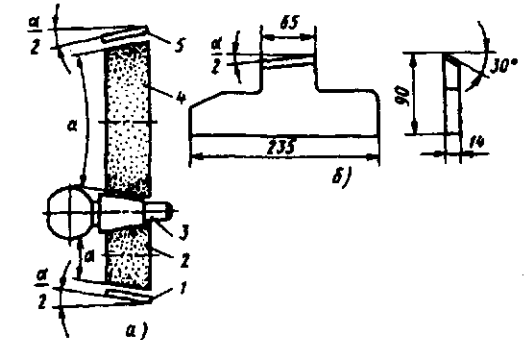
Схема наладки для шлифования конуса: а – схема наладки; б – опорный нож; 1 и 5 – копирующие линейки; 2 – ведущий круг; 3 – обрабатываемая деталь; 4 – шлифовальный круг
